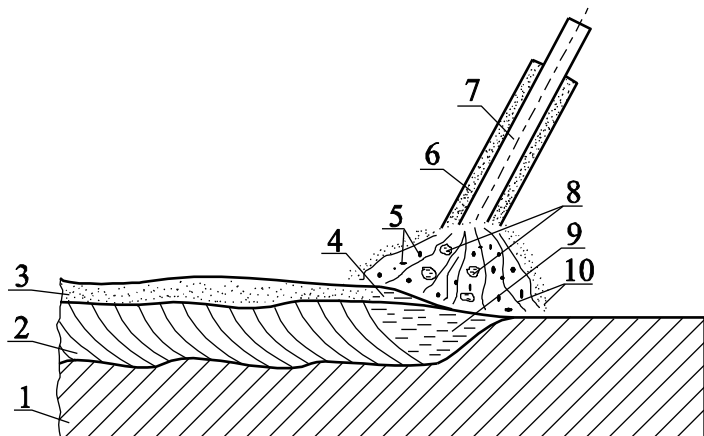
Схема сварки плавящимся электродом.
